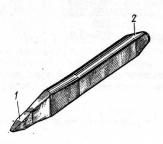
1—рабочая часть; 2 ударная часть Используются для разделки кромок свариваемых элементов под сварочные швы при производстве электрогазосварочных работ.
